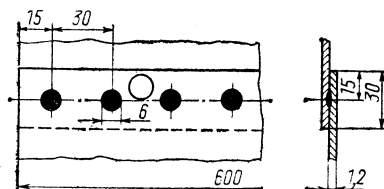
Шов двухрядной точечной сварки
